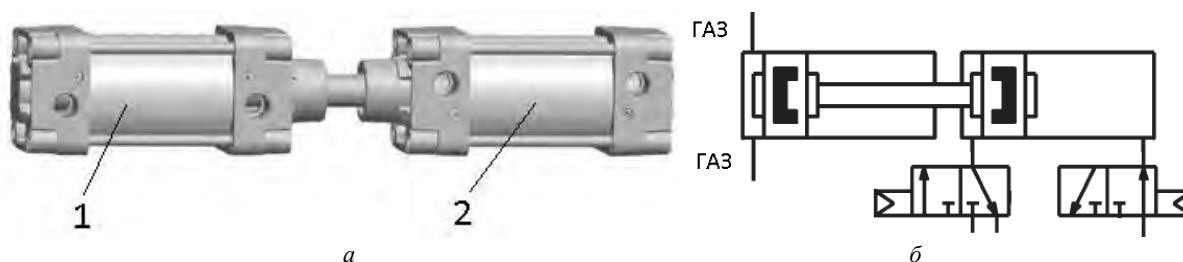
Типовий опозитний пневмоциліндр (а) та пневматична схема циліндра-дозатора (б)
